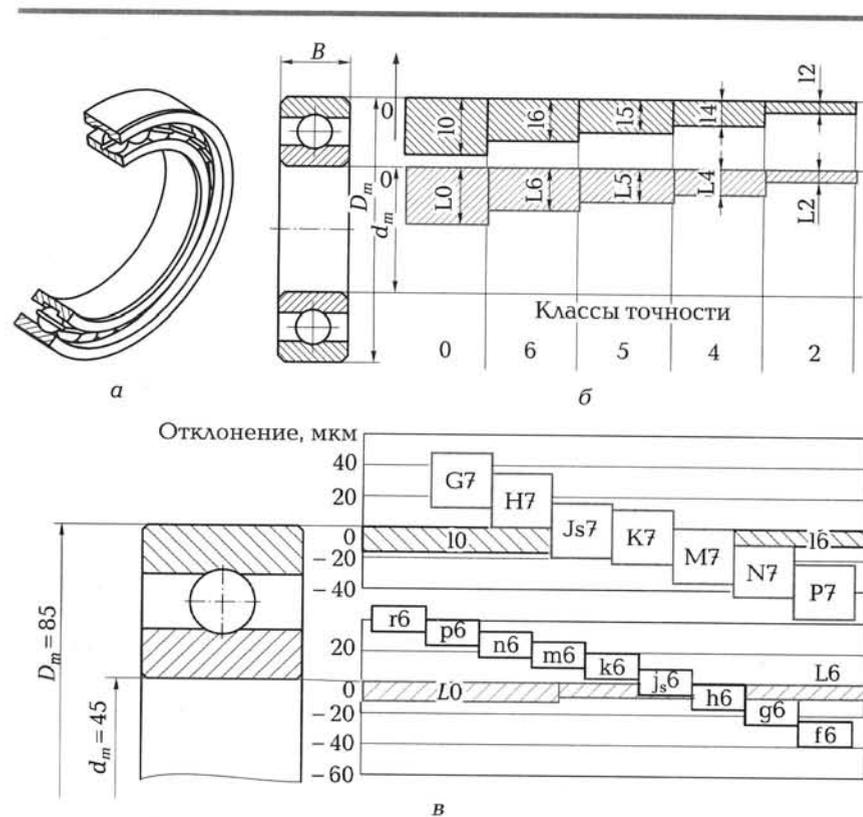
Подшипник качения (а), схемы расположения полей допусков диаметров колец подшипника (б) и полей допусков посадочных поверхностей (в) вала и отверстия в корпусе
